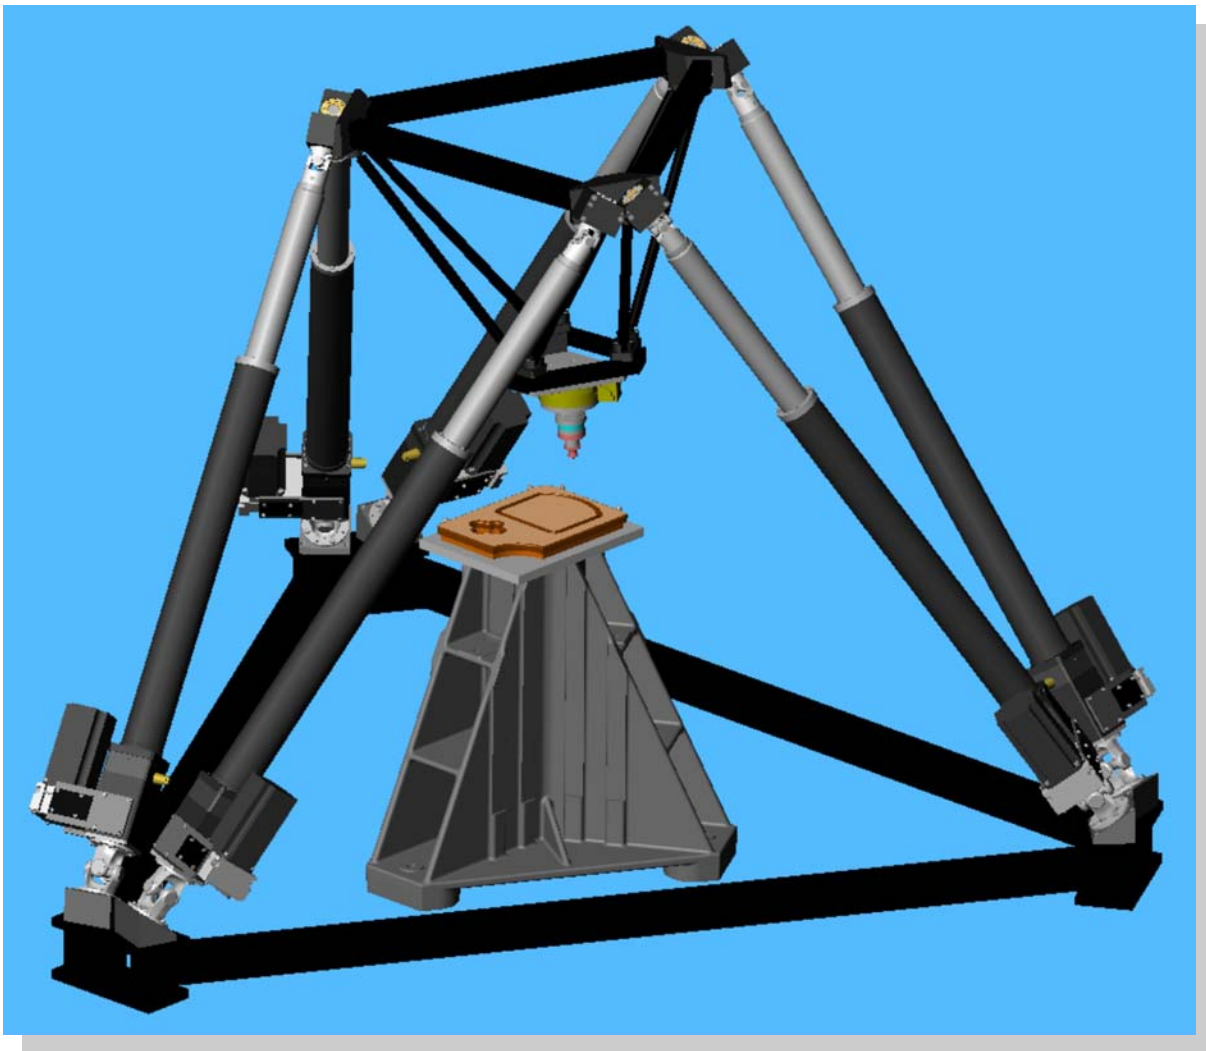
Hexapod "FELIX" mit Glättwerkzeug und Werkstück-Spannvorrichtung
